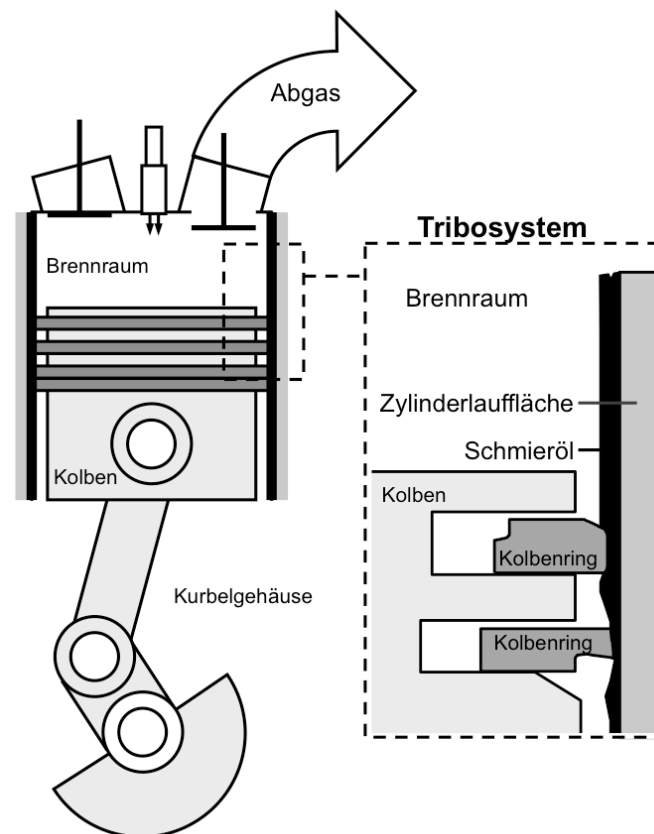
Das Tribosystem, bestehend aus Kolben, Kolbenring und Zylinderlauffläche:
